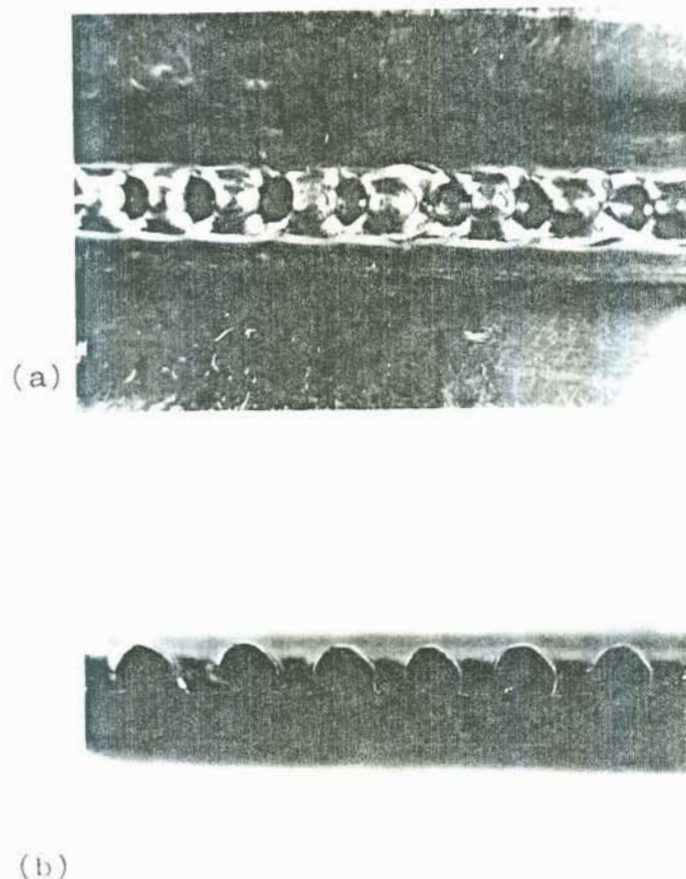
Aspecto de uma solda com corcova; (a) vista superior da formação no cordão de solda e (b) corte longitudinal mostrando a penetração.
